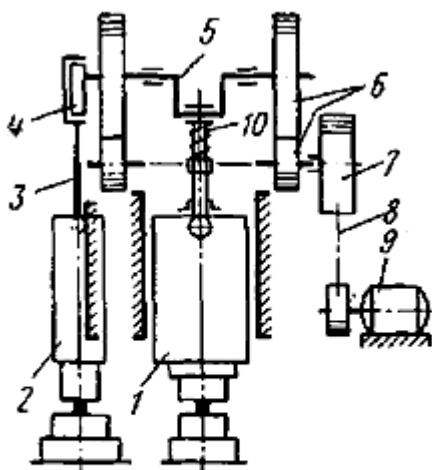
Кинематическая схема кривошипного обрезного прессы: 1 – ползун; 2 – боковой ползун; 3 – шатун; 4 – эксцентрик; 5 – эксцентриковый вал; 6 – зубчатая передача; 7 – маховик; 8 – клиноременная передача; 9 – электродвигатель; 10 – основной шатун.
